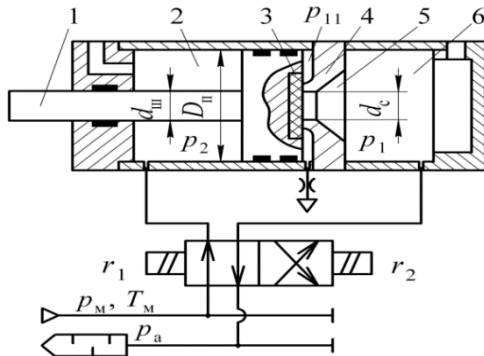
Схема ударного пневмоагрегата (базова)
